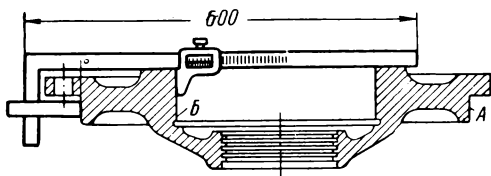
Приспособление для проверки concentricности посадочных поверхностей подшипникового щита
